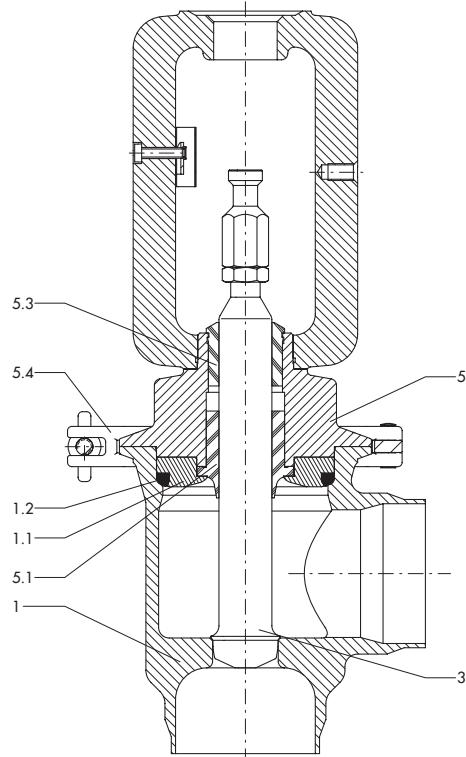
· Клапан тип 3347, исполнение с литым корпусом
